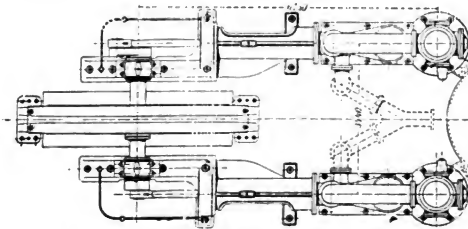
Längsangehender Motor mit Pumpe. Grundriss.
